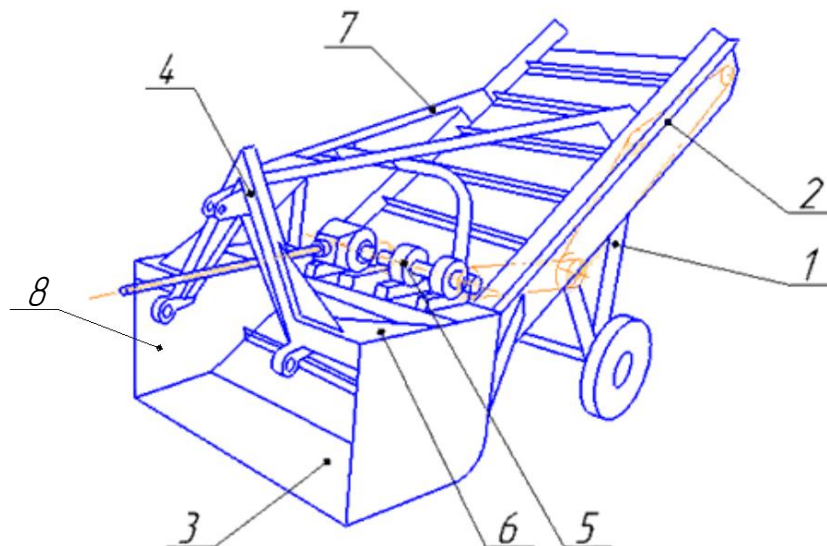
Схема навесной машины для удаления и погрузки почвы в теплицах: 1 - несущая рама; 2 – транспортёр планчатый; 3 – ковш; 4 - механизм навески; 5- механизм привода; 6 –верхняя стенка ковша; 7 - верхняя тяга; 8 - отвал
